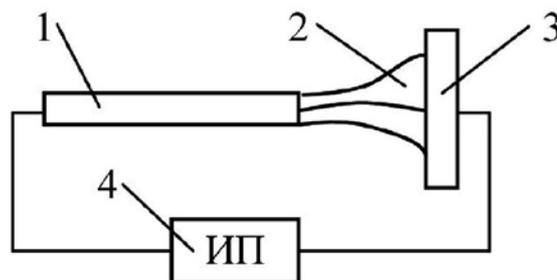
Схема цепи дуговой сварки или плавки:
